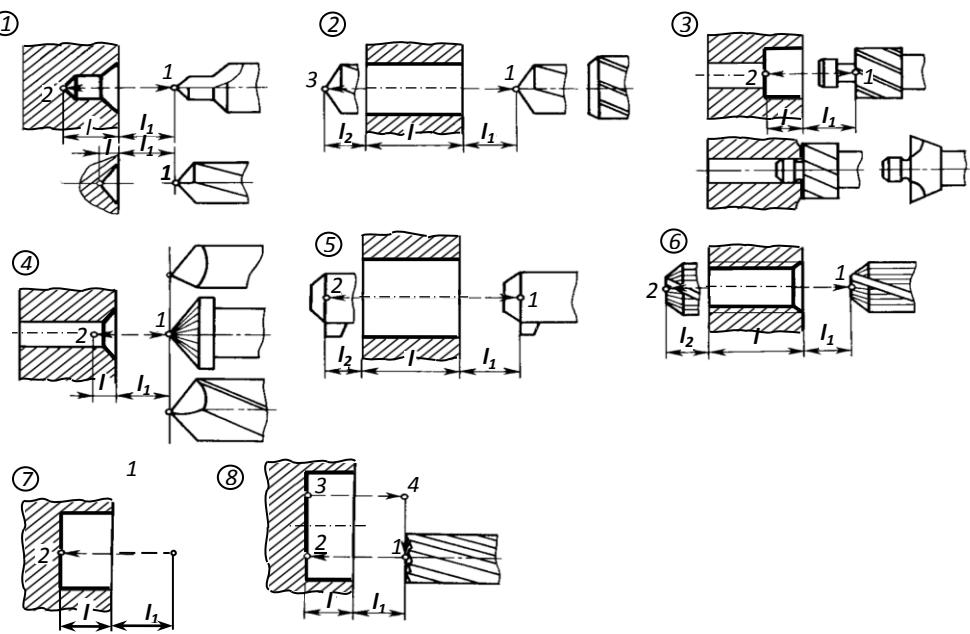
Типові переходи обробки внутрішніх циліндричних поверхонь:
